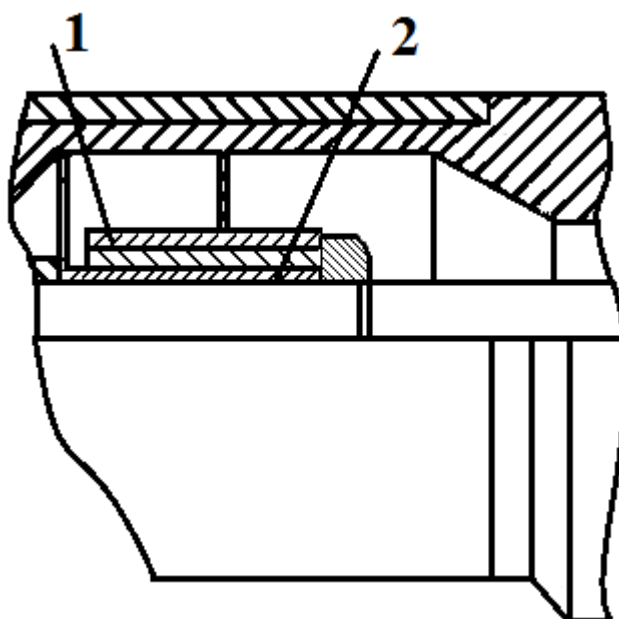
Радиальный подшипник ЭЦН. 1 – неподвижная втулка с вкладышем; 2 – вращающаяся с валом втулка.
